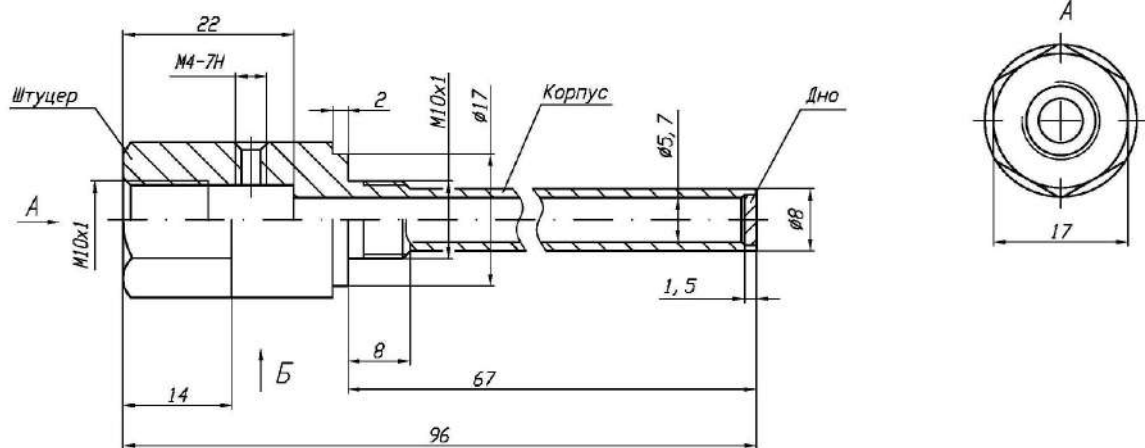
Габаритный чертеж цельноточеных с вварным дном защитных гильз
